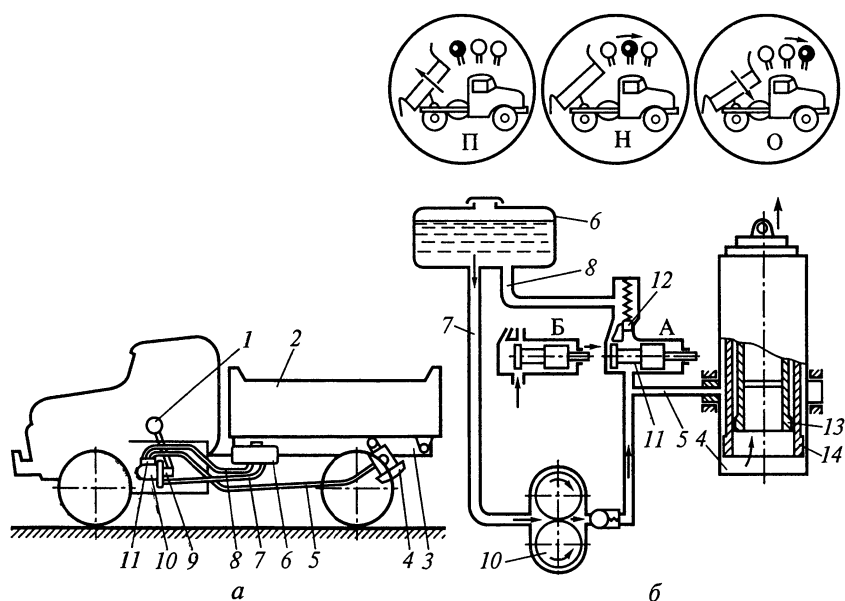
Гидравлический подъемный механизм самосвалов ЗИЛ-ММЗ: а — схема размещения на автомобиле; б — схема механизма; 1 — рычаг; 2 — кузов; 3 — надрамник; 4 — гидроцилиндр; 5, 7, 8 — трубопроводы; 6 — масляный бак; 9 — коробка отбора мощности; 10 — насос; 11 — кран управления; 12 — клапан; 13, 14 — звенья; П, Н, О, А, Б — положения золотников
